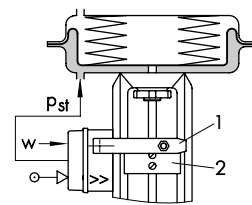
Sentido de actuación >> Montaje a la izquierda
